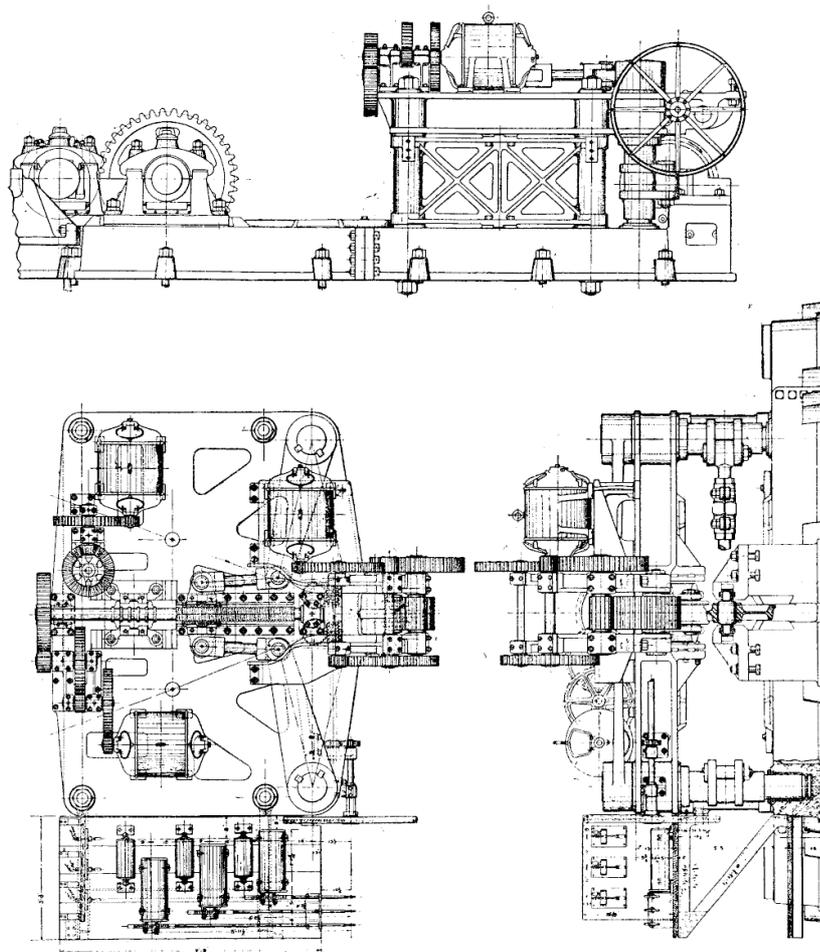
, 3 et 4. — Laminoir *Schoen*. Élévation, plan et bout partout.
